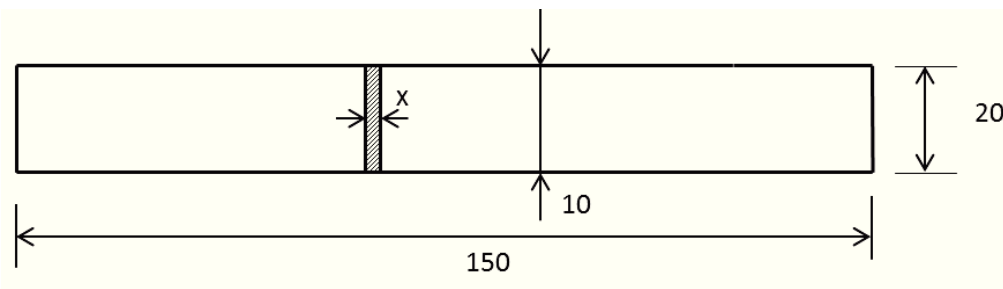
Dimensões do provete utilizado para ensaio de flexão
